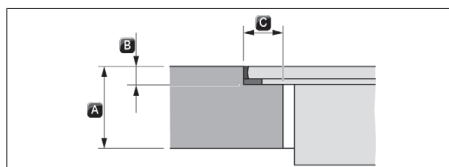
Dimensiones de rebajo para instalación enrasada
